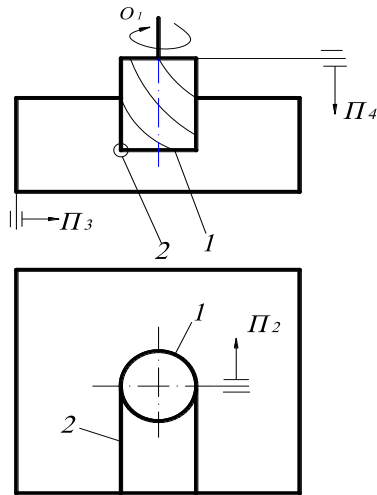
Схема фрезерування паза кінцевою фрезою
